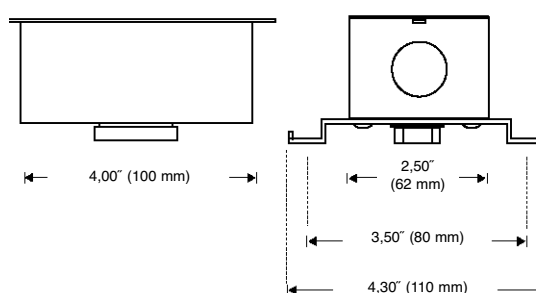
Les dimensions de la sonde de température TE-704 C/D sont exprimées en pouces et en millimètres (mm).
